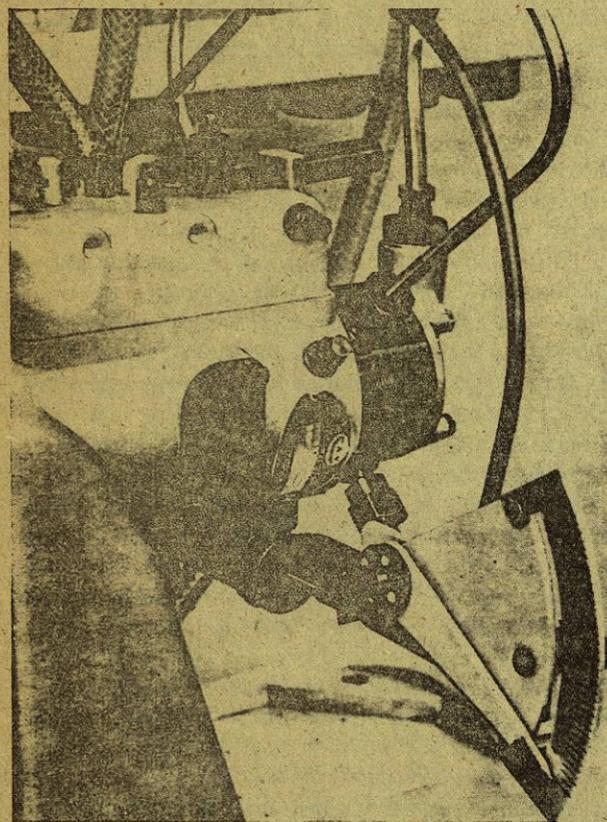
Herramienta de comprobación del avance de leva montada en una bomba
